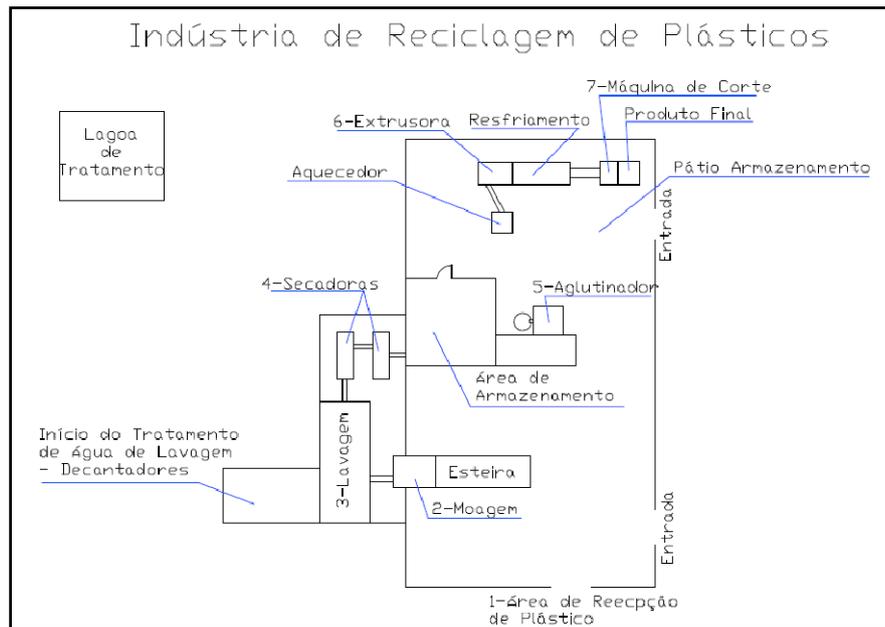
LXX: Croqui da ERPLASUL – layout e equipamentos
